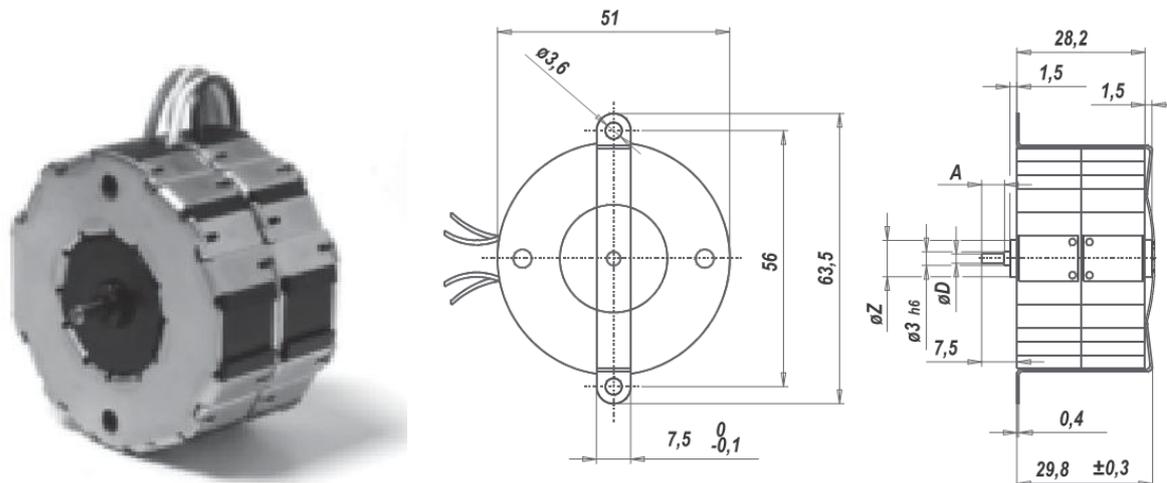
Motor paso a paso UFD a) Motor físico b) Dimensiones
